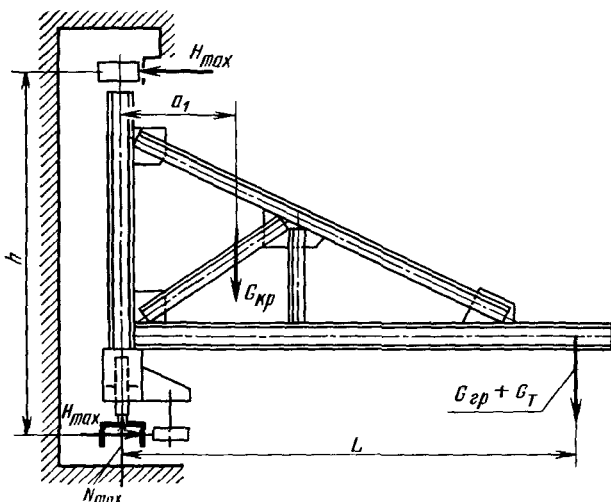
Расчетная схема определения нагрузок на опорные колеса настенного консольного передвижного неповоротного крана
